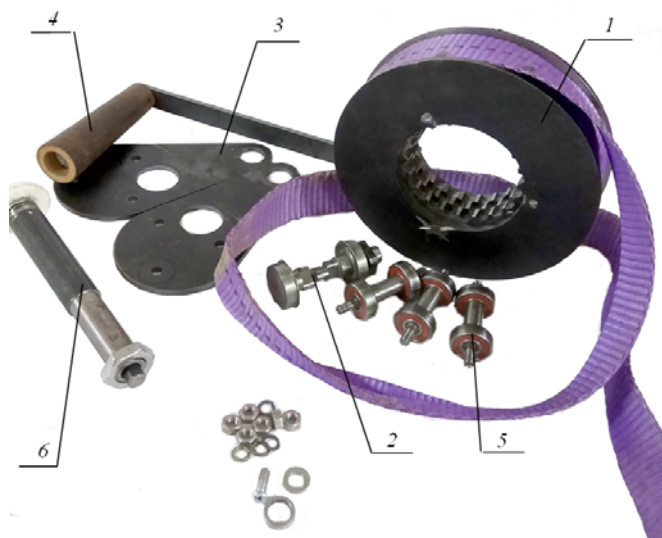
Детали ручной лебедки, смонтированной на основе эксцентриковой передачи с числом контактных пар в зацеплении, равном 3: 1 – барабан, состоящий из набора зубчатых колес; 2 – эксцентрик с подшипниками, запрессованными в крышки; 3 – реборда; 4 – ручка; 5 – вал с подшипниками; 6 – фиксирующий механизм
